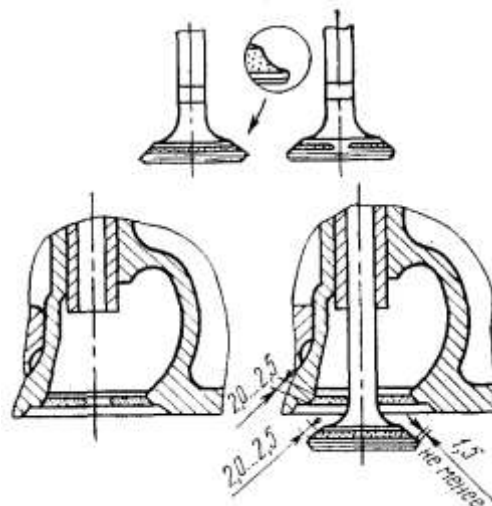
Обработка седла клапана с помощью приспособления - ОПР-1334А.
